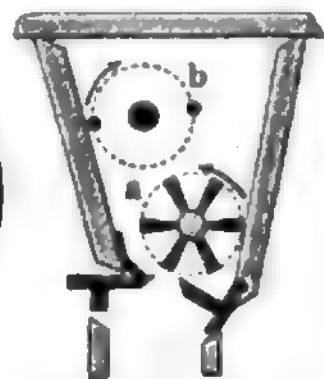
Düngerstreumaschine von Gampel. Fig. 2. Querschnitt des Kastens.
